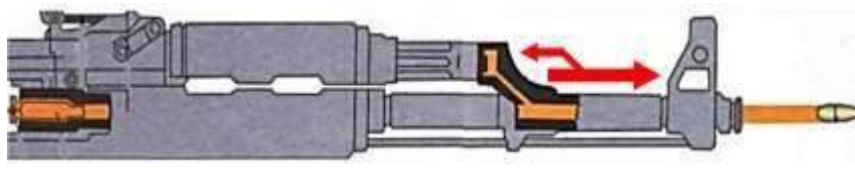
Схема руху порохових газів в автоматі Калашникова
